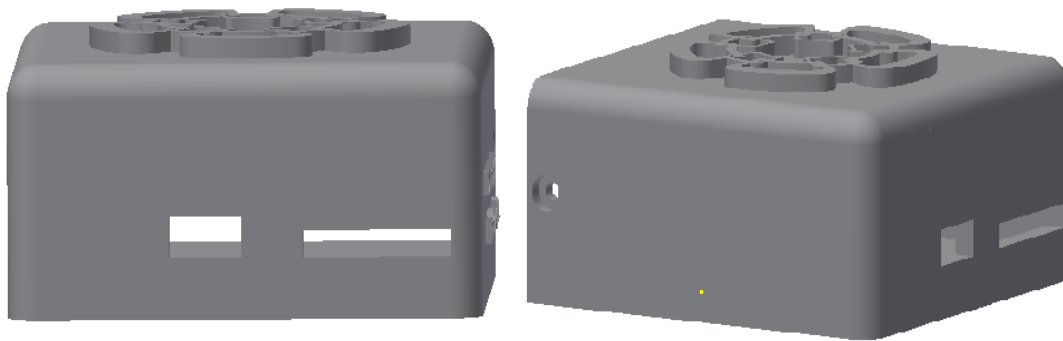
Vista frontal y vista lateral izquierda de la imagen del diseño 3D para el montaje del sistema RCAD.
